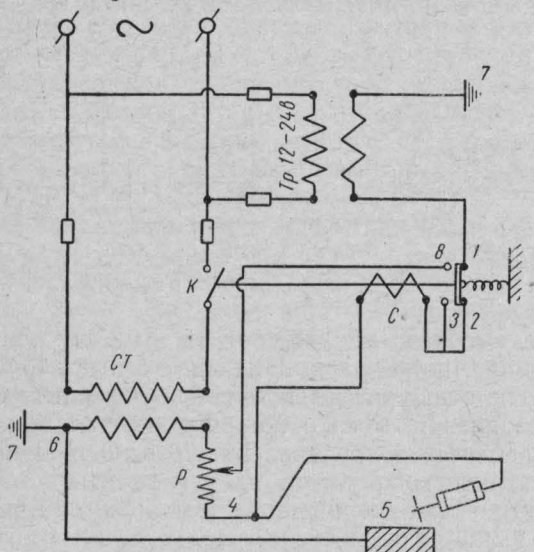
Схема автоматического отключения сварочного трансформатора.
